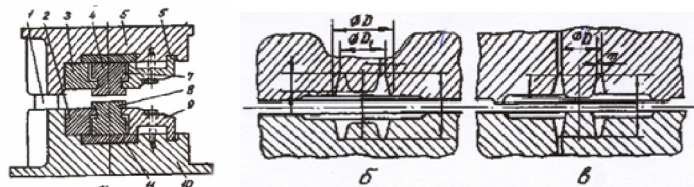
Сборочный штамп для штамповки на КГШП:
